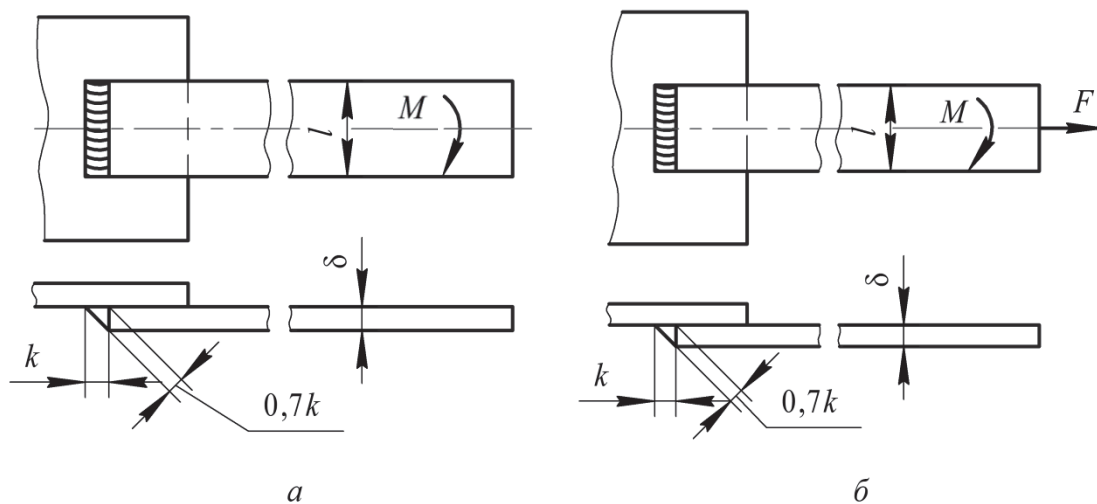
Сварное соединение угловым швом, нагруженное:
